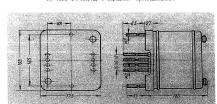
Габаритные и установочные размеры реле типа ЭТ-523/1Д с задиим присоединением
